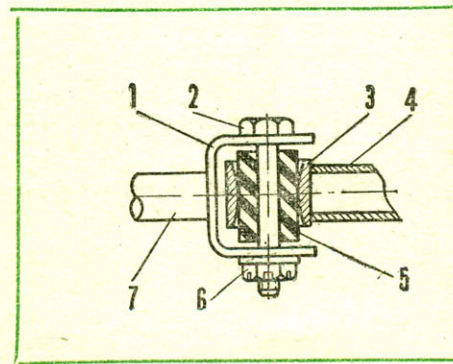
Рулевой шарнир: 1 — проушина (сталь 3); 2 — соединительный шарнирный болт М8; 3 — кольца шарнира (сталь 3); 4 — поворотный рычаг; 5 — втулка (резина); 6 — корончатая гайка М8; 7 — труба поперечной тяги.
